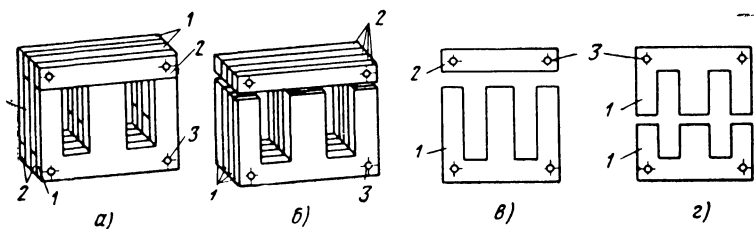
Штампованные пластины сердечников и их сборка: а — сборка вперекрышку, б — встык, в — разъем по яру, г — разъем по стержню; 1 — Ш-образные пластины, 2 — замыкающие, 3 — отверстия под шпильки.
